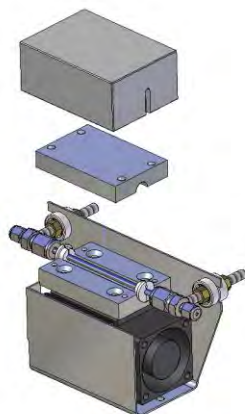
Explosionszeichnung des Peltier-Kühlers
